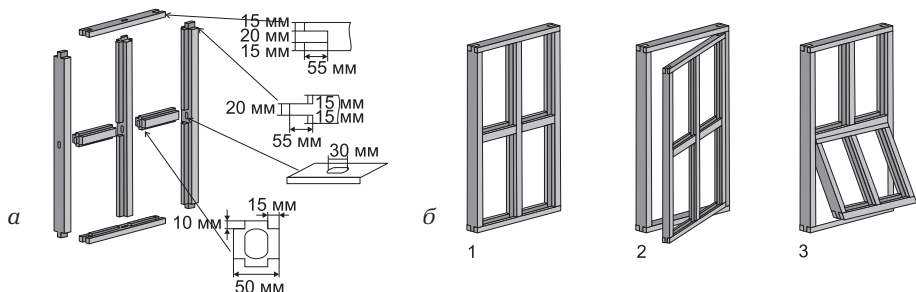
Сборка деревянных рам (а) и внешний вид рам с дверью и форточкой (б): 1 — рама для стекла; 2 — встроенная дверь; 3 — форточка
